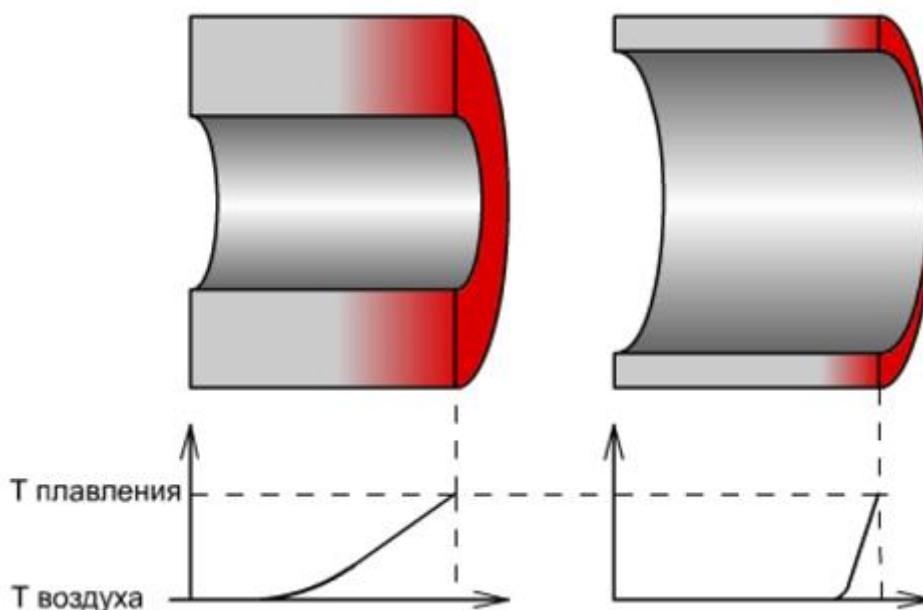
«Температура сварочного зеркала для ПП»
